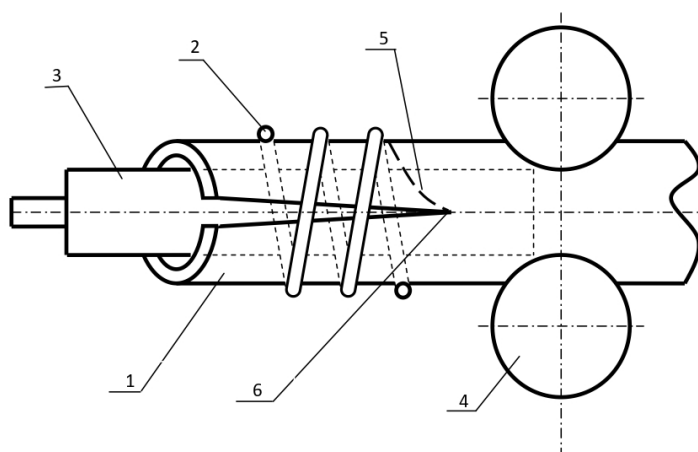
Схема высокочастотной сварки с индукционным подводом тока к кромкам трубной заготовки: 1 – трубная заготовка; 2 – кольцевой двухвитковый индуктор; 3 – ферритный стержень; 4 – валки сварочной клетки; 5 – путь тока; 6 – точка схождения кромок
